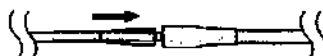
Установка страховочной муфты на соединительный ниппель.
